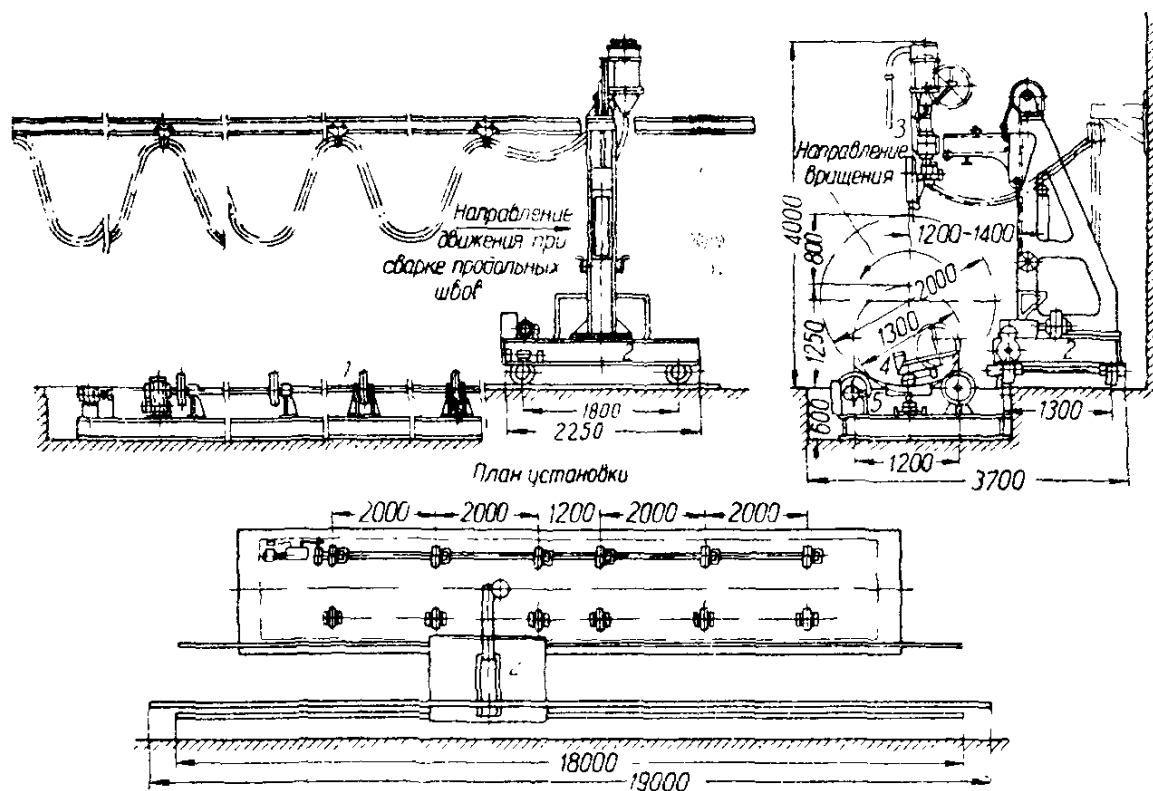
Автоматическая установка для сварки двутавровых балок.
